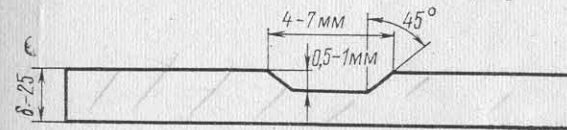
Форма канавки подкладной планки для сварки автоматом.
